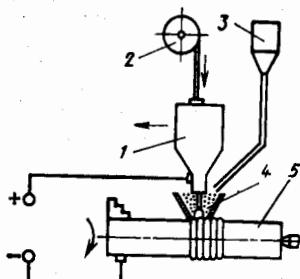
Схема автоматической дуговой наплавки деталей под флюсом
